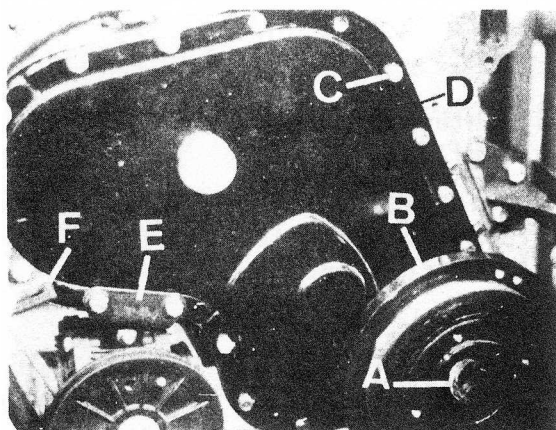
Desmontaje de la tapa de la distribución y damper
